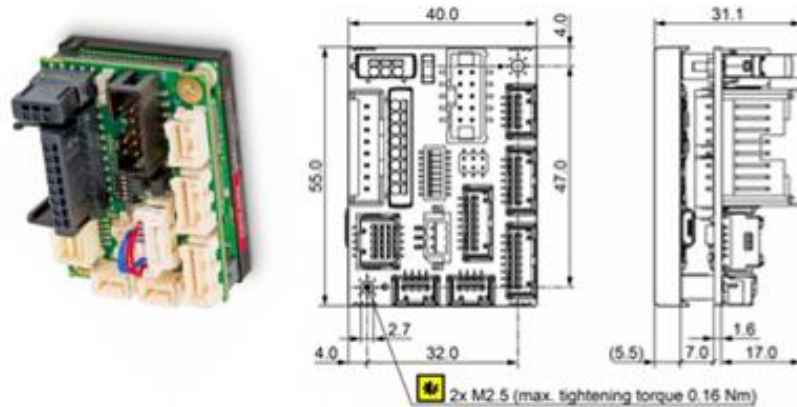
Dibujo dimensional de la EPOS4 Compact en mm. [29]
